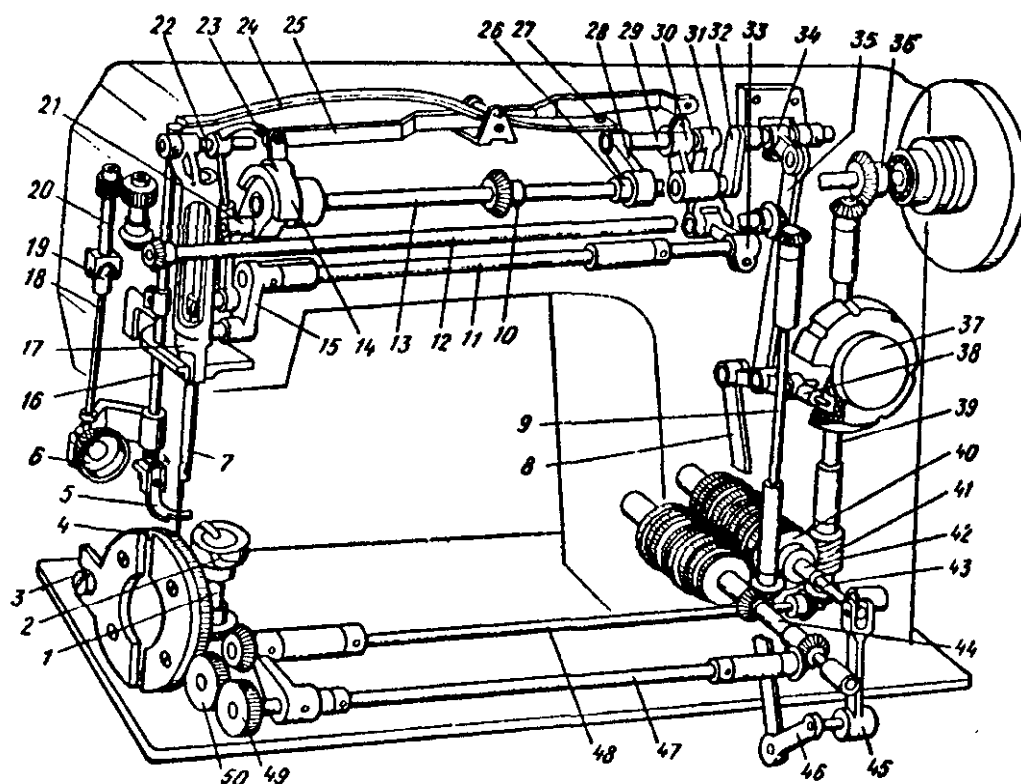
Схема швейной машины кл. 330-8 ПМЗ
